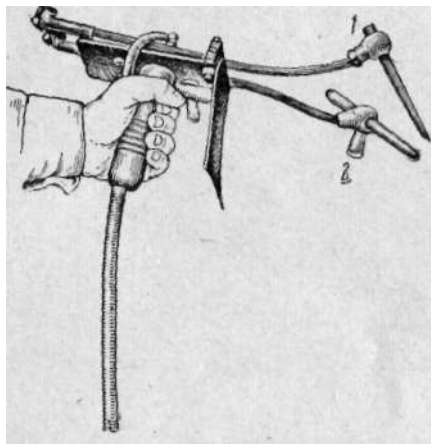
Ручной плавильный аппарат с углеудерживающими (1 и 2) приспособлениями для получения вольтовой дуги.
